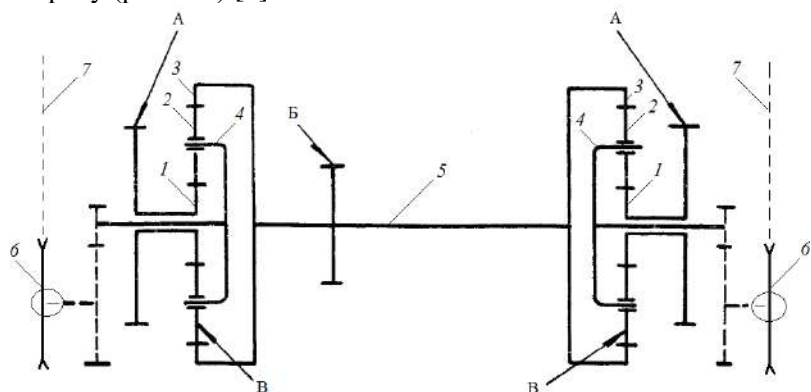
Концепція двопотокового механізму повороту:
